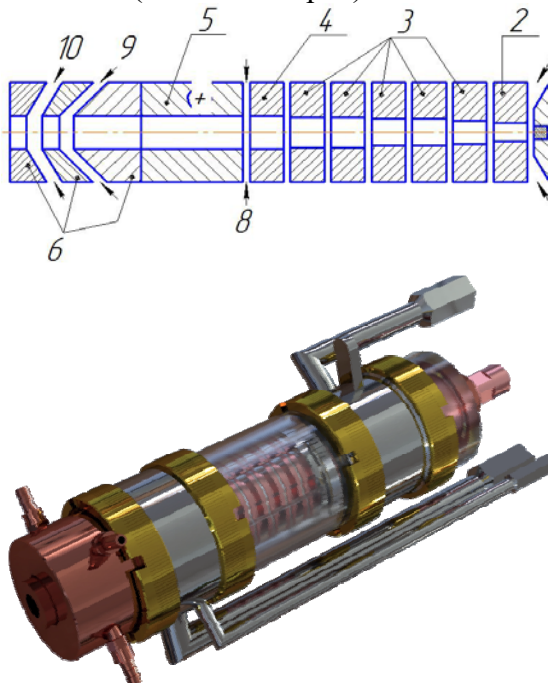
Схема и внешний вид плазмотрона «ПНК – 50»
